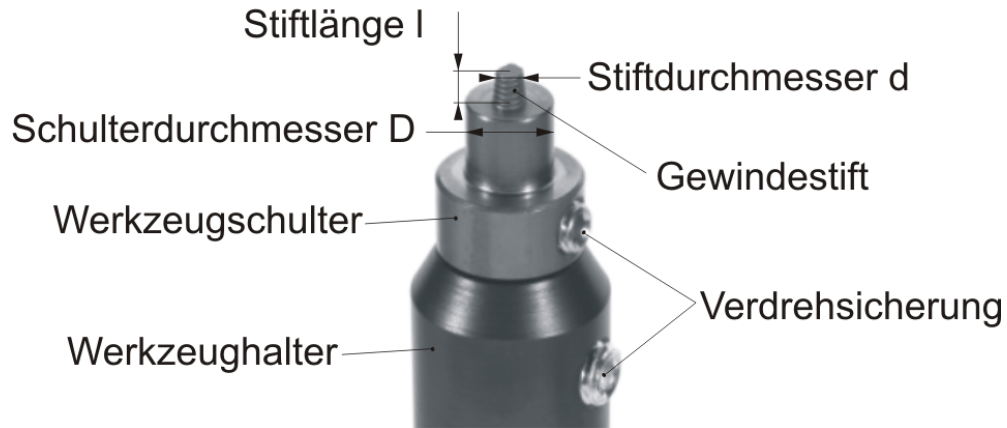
Beispiel für ein Werkzeug mit Wechselstift [65]
